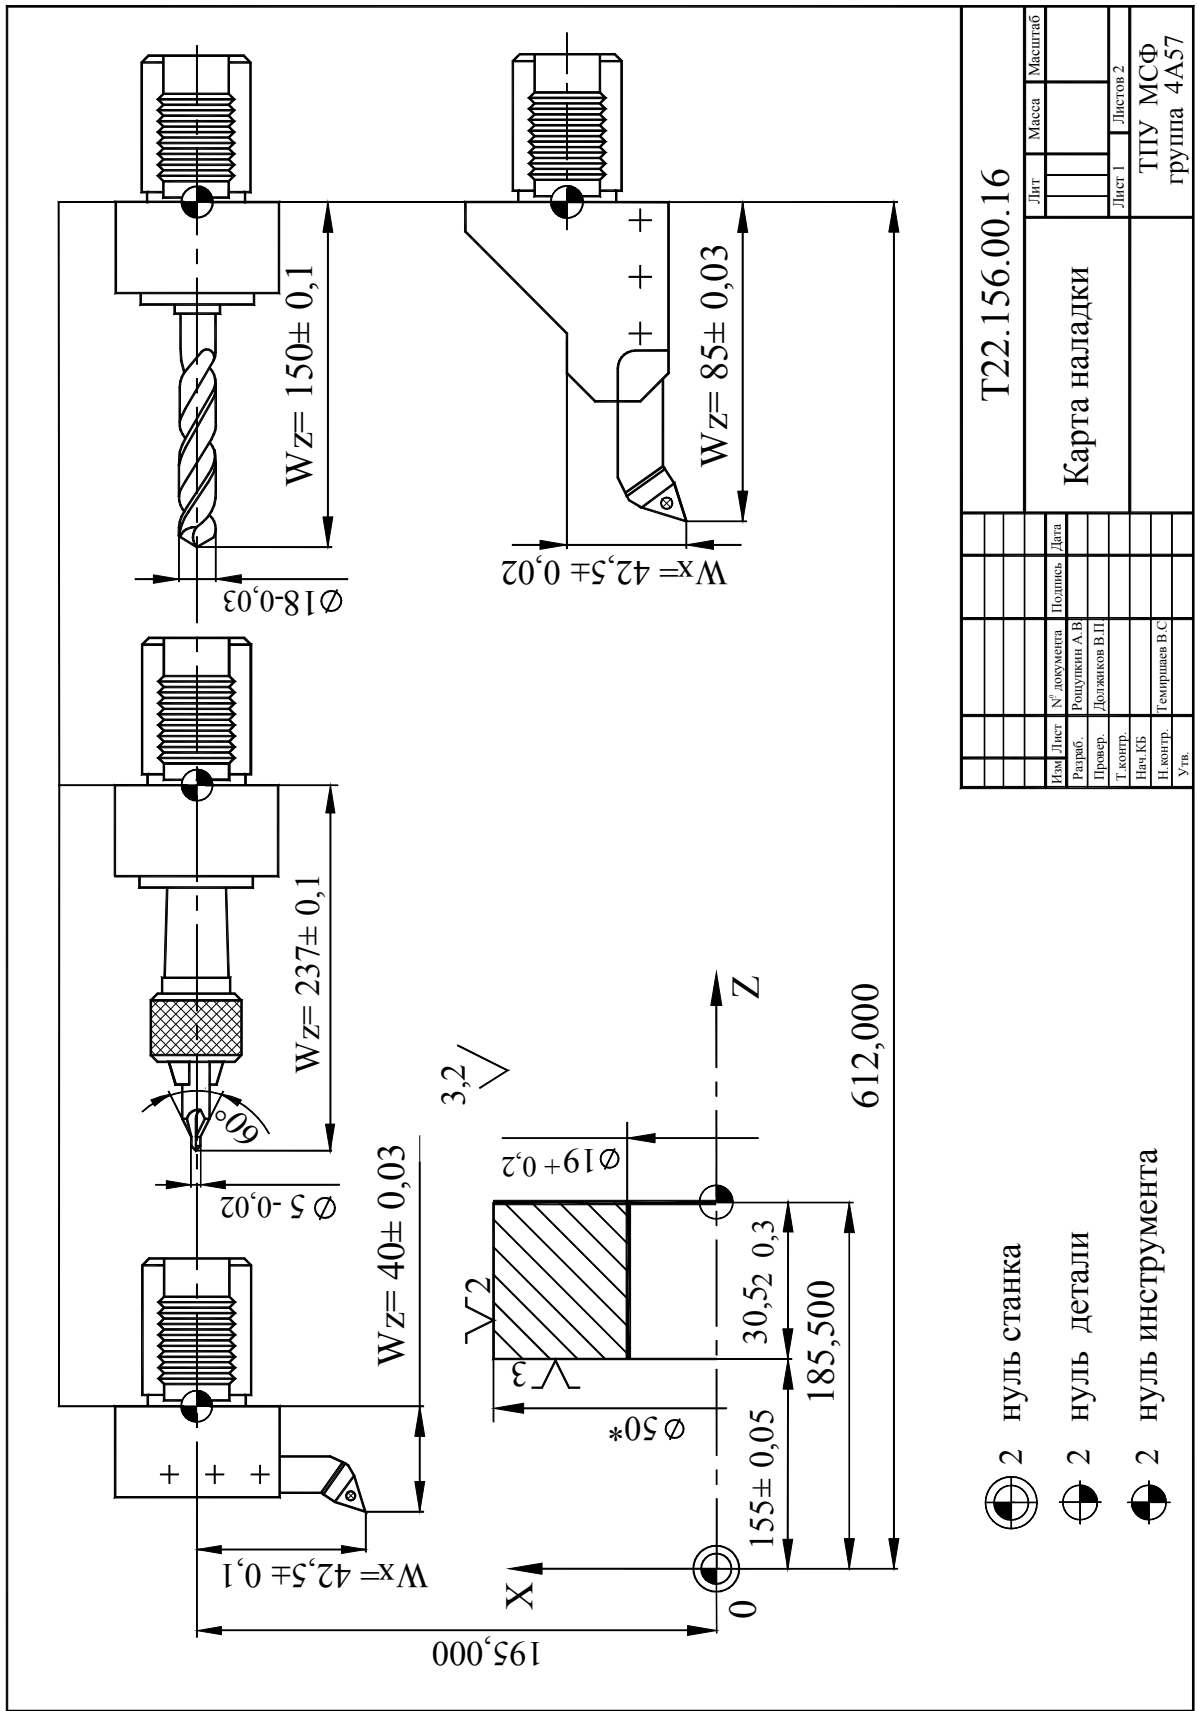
Эскиз карты наладки для токарного станка с ЧПУ модели СПИ220АП
